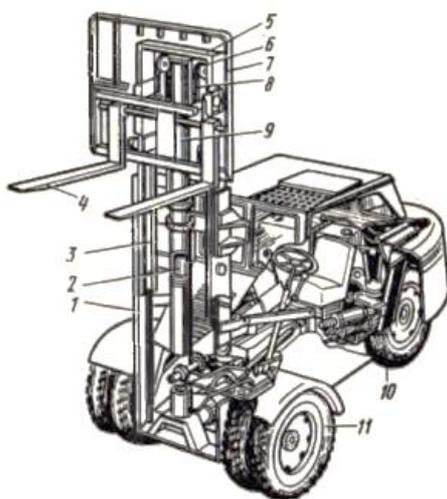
Автопогрузчик: 1 – опорная рама; 2 – гидроподъемник; 3 – телескопическая рама; 4 – вилочный захват; 5 – поперечина; 6 – звездочка; 7 – каретка; 8 – грузовые цепи; 9 – плунжер; 10 – колеса; 11 – сдвоенные колеса.
